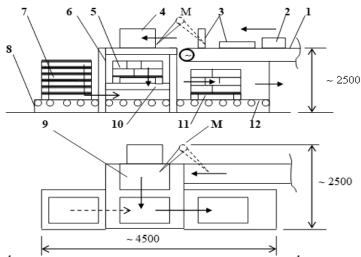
Пакетоформирующая машина с горизонтальным формированием слоев грузов: 1 — конвейер подачи грузов; 2 — грузы; 3 - ориентирующие устройства; 4 — сталкиватель слоев (или манипулятор М); 5 —формируемый пакет; 6 — корпус (металлоконструкция); 7 — магазин пустых поддонов; 8- конвейер подачи пустых поддонов; 9 - устройство формирования слоев; 10 - подъемная платформа (снижатель); 11-сформированный пакет; 12 - конвейер выдачи готовых пакетов
